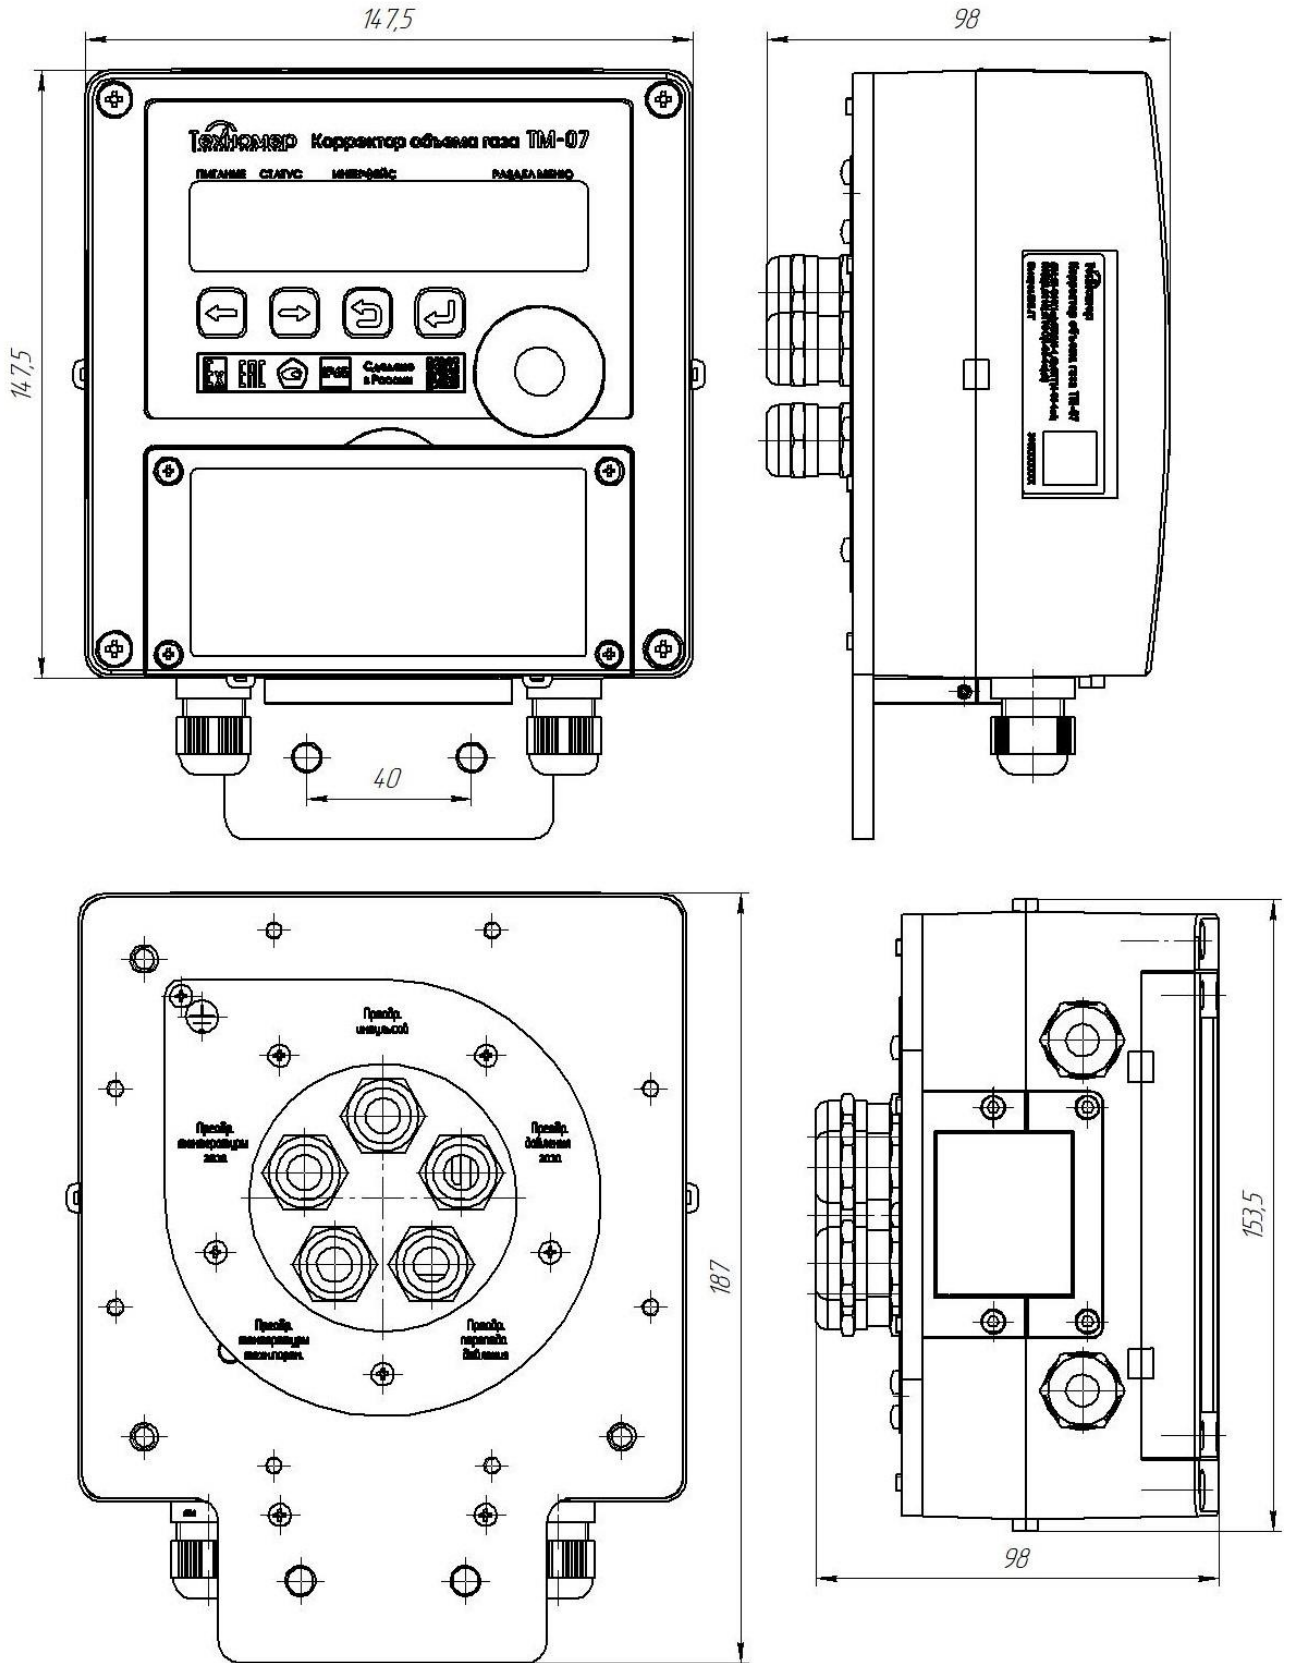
Габаритные размеры корректора без установочного комплекта
